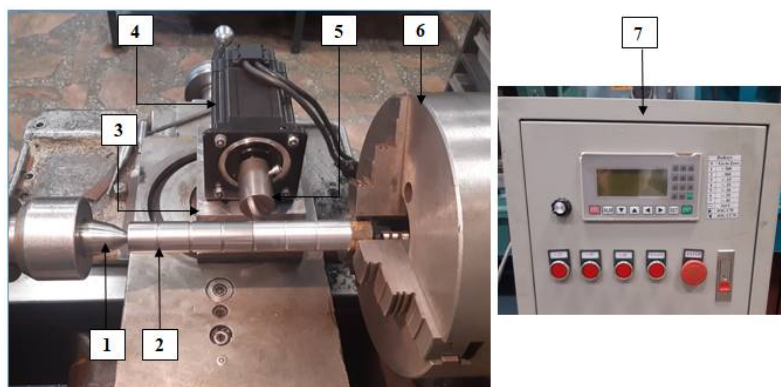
Общий вид устройства для реверсивного поверхностного пластического деформирования наружных поверхностей цилиндрических деталей на токарном станке *1К62*:
